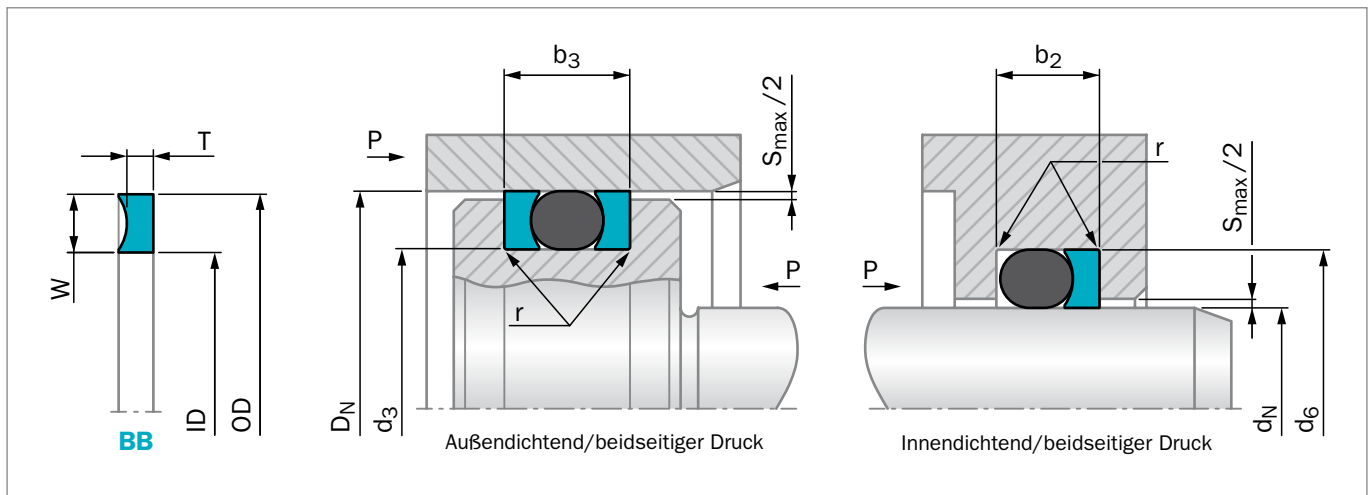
Einbauzeichnung innendichtend und außendichtend, konkaver Stützring-Typ BB
